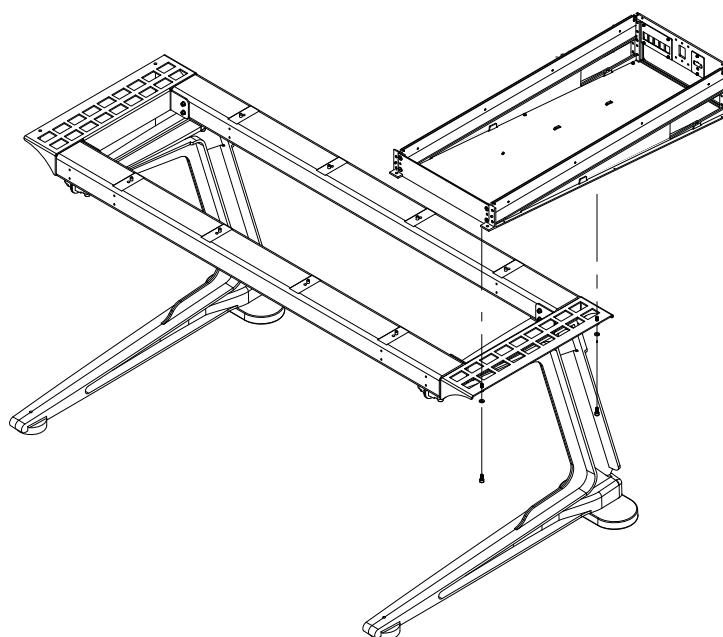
Fixation du premier bac sur les entretoises d'un châssis sur pieds
